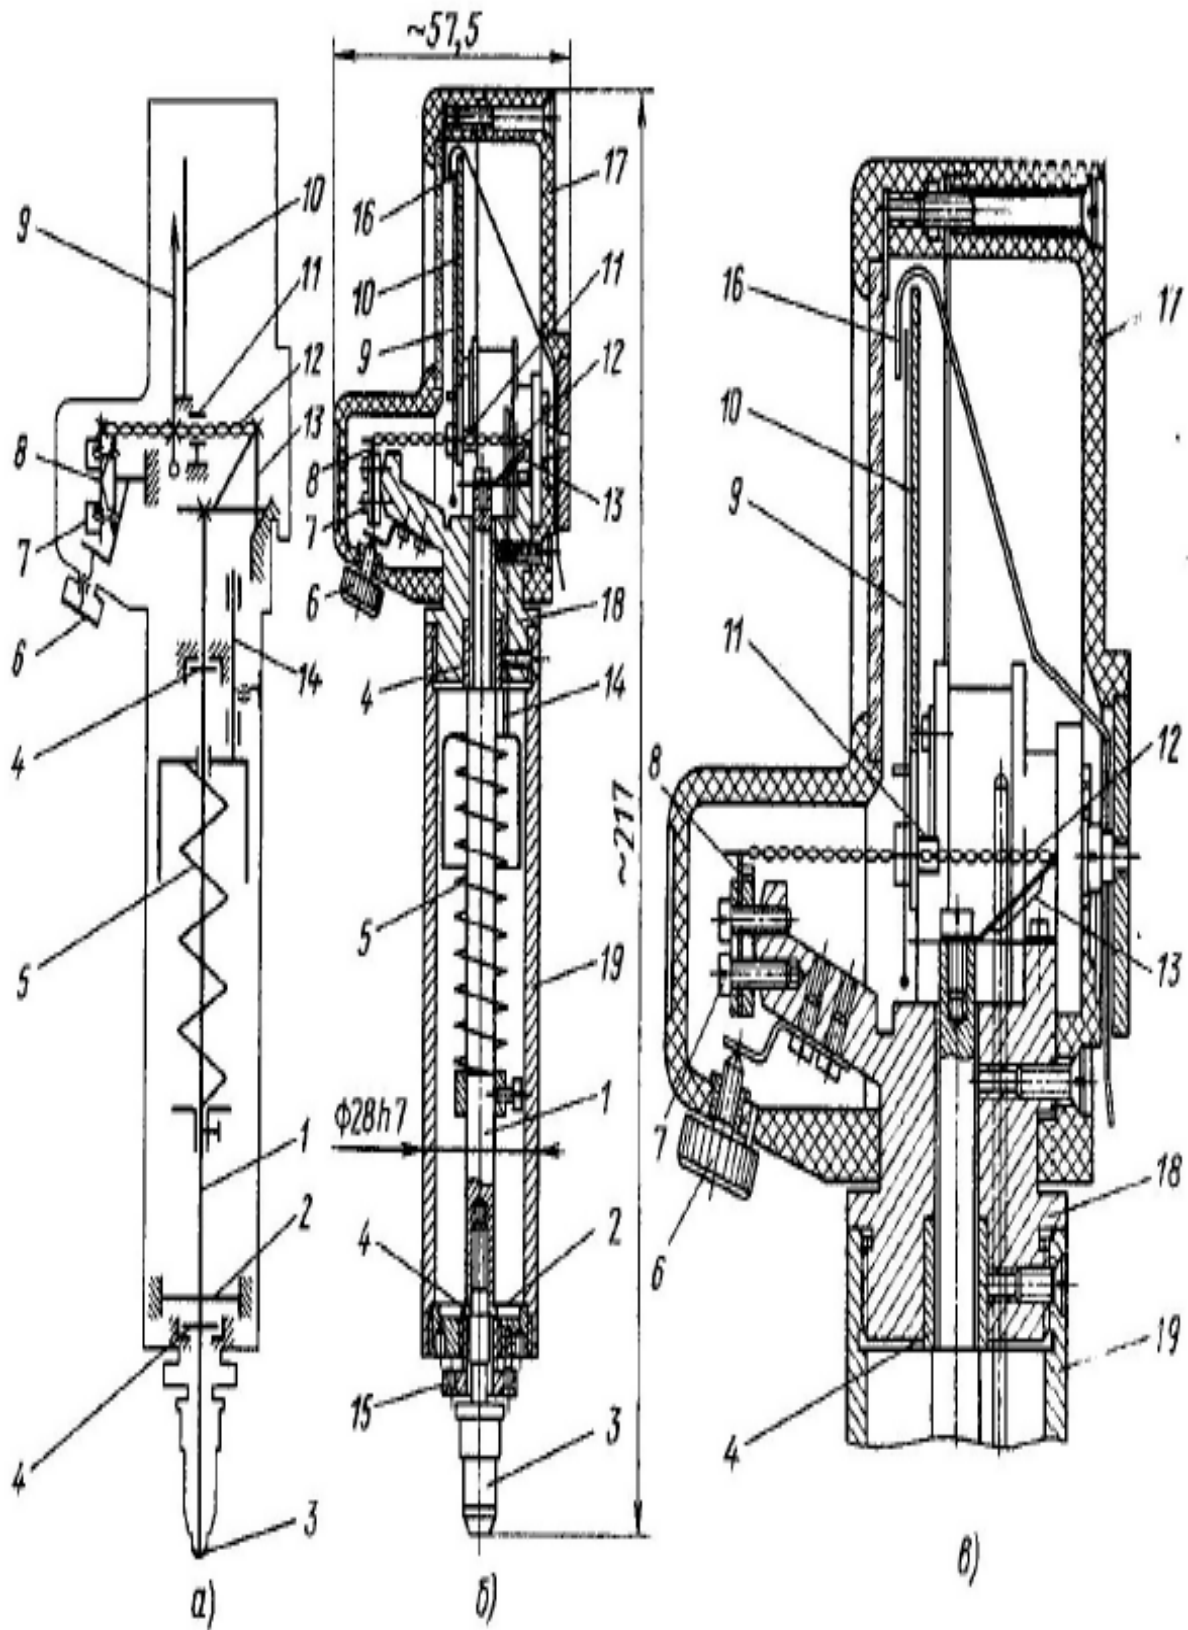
Пружинная измерительная головка (микрокатор): а- схема; б- конструкция микрокатора; в-конструкция верхней части микрокатора
